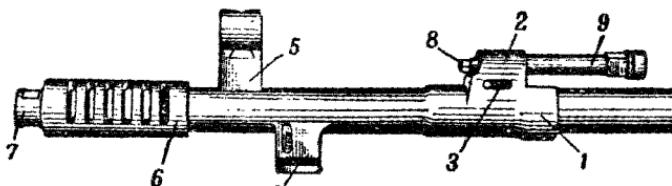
Надульник СВТ-40: 1 - рас труб; 2 - газовая камора; 3 - поперечное овальное отверстие; 4 - нижний выступ; 5 - верхний выступ; 6 - дульный тормоз; 7 - втулка дульного тормоза; 8 - регулятор; 9 - патрубок.
